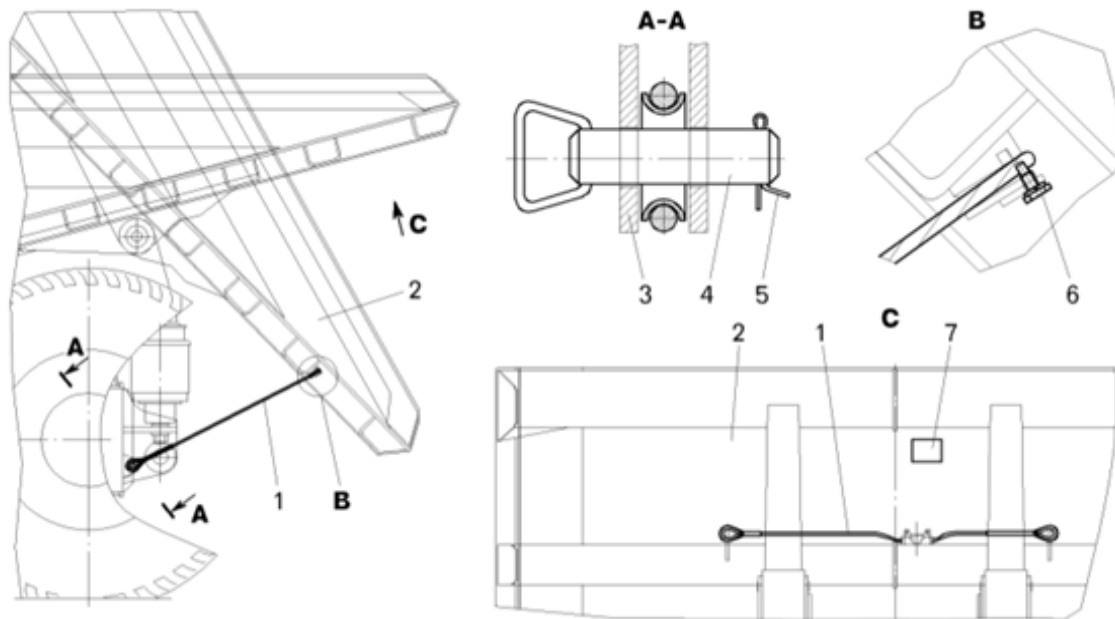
Схема строповки: 1 – трос для стопорения платформы; 2 – ГП; 3 – проушина картера заднего моста для крепления троса; 4 – шкворень (буксирный палец); 5 – шплинт; 6 – стопорный болт; 7 – табличка предупреждения
